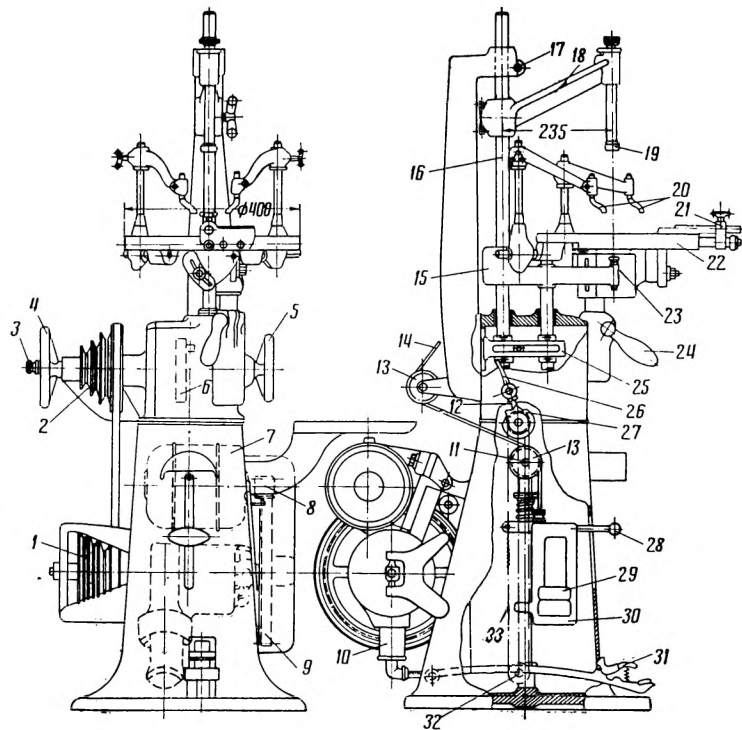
Кинематическая схема опилочного станка завода «Коммунар»
